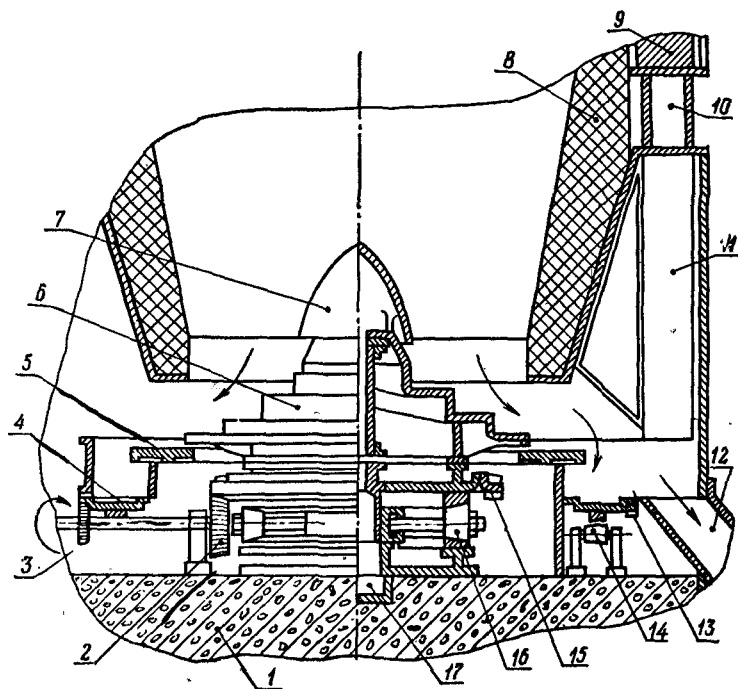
Устройство для выгрузки извести из шахтной печи.
